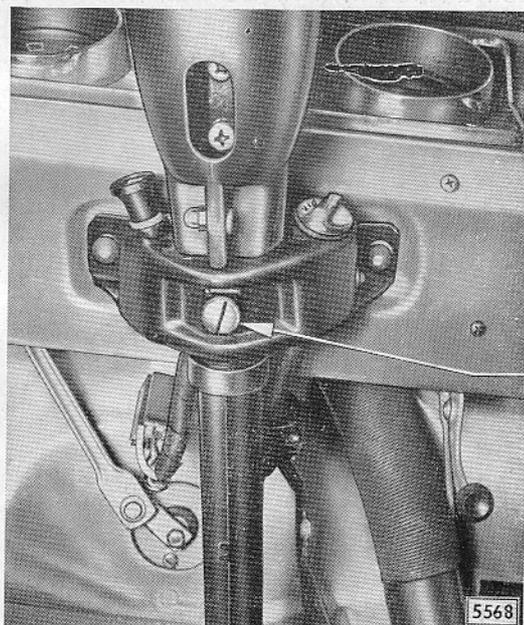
Anschlagsschraube für Lenkspindel im Lenkstützrohrhalter
